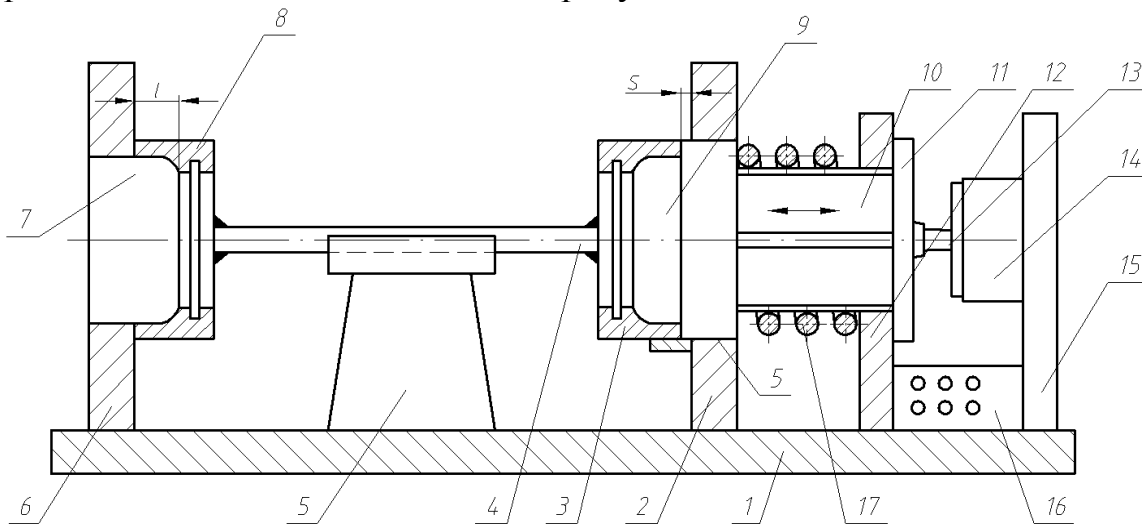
Пристрій для зварювання секцій РО ГГК:
